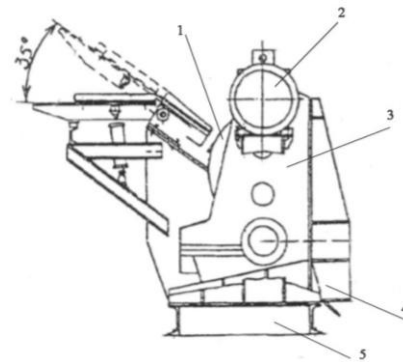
Загальний вигляд одноопераційного ріжучого пристрою
